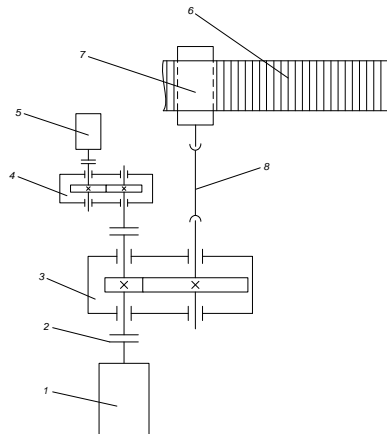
Кінематична схема приводного механізму оберткової печі СМЦ-26
